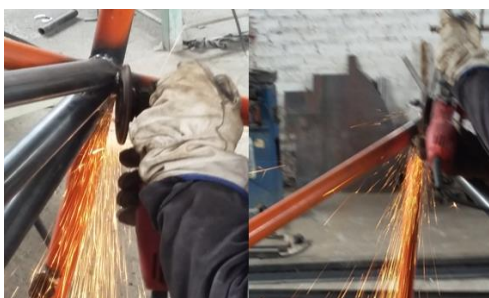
Ubicación de la Pistola sobre la Superficie a Soldadura
